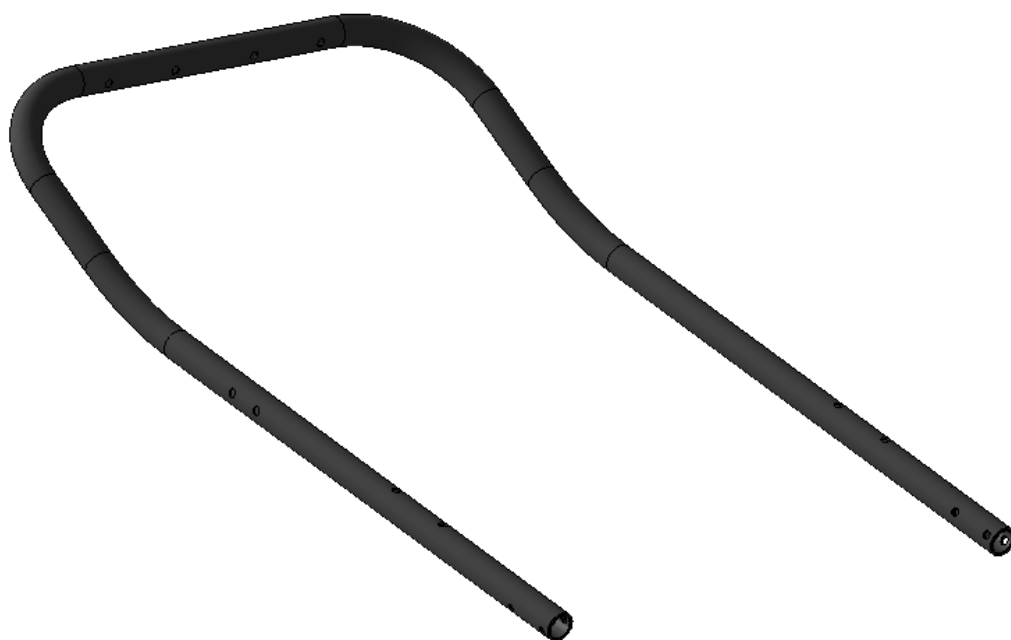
Detalle inferior perforación tubo bastidor en placa ensamblaje
